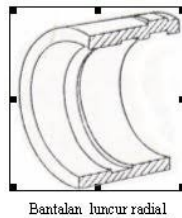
Bearing* dan Rumah *Bearing
